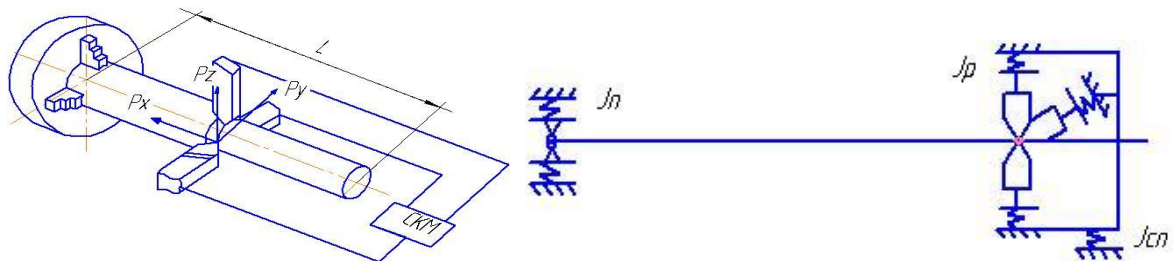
Схема обробки циліндричної деталі трирізцевою головкою.
